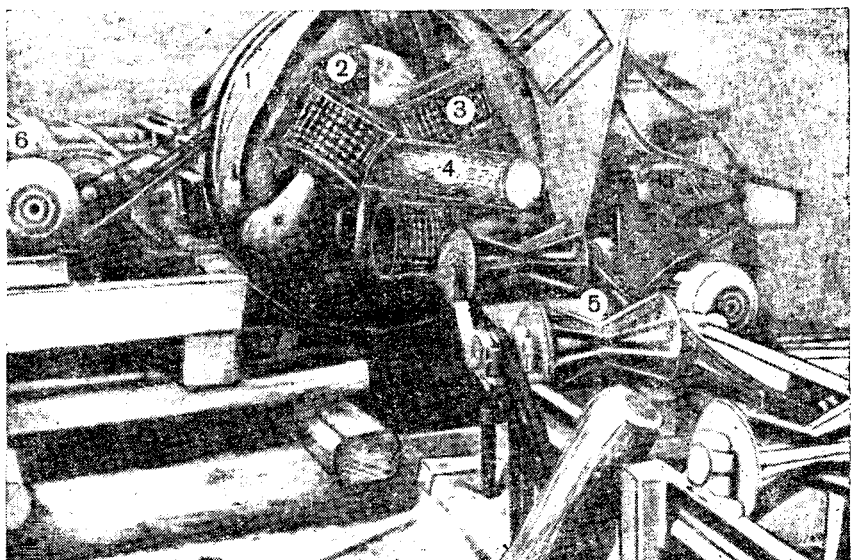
Станок ЦНИИМЭ с шестью наколочными барабанами:
